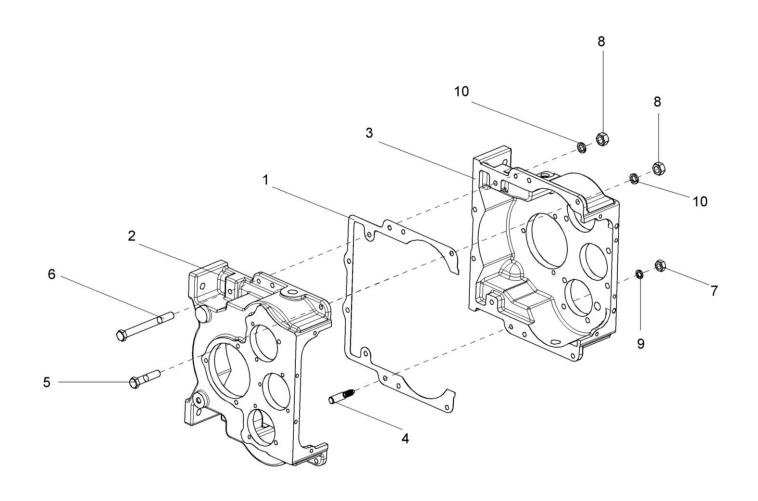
Корпус коробки диапазонов 3518020-46170
